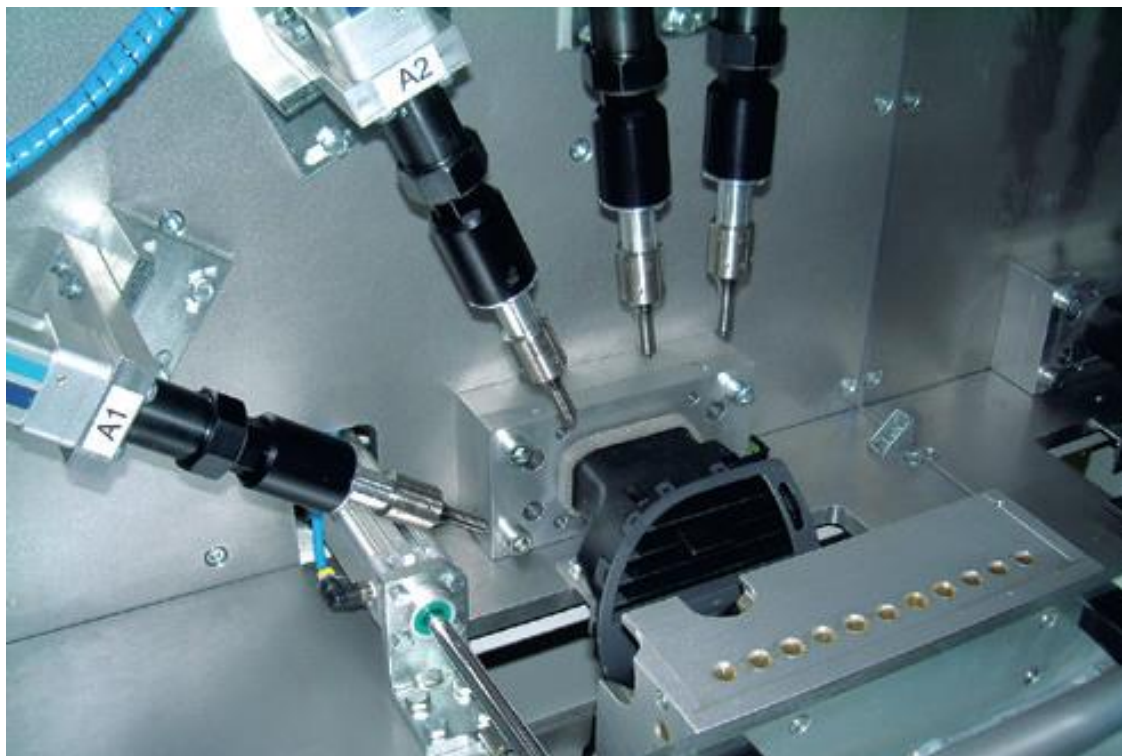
Многоточечная машина для ультразвуковой сварки компании «U-Sonic»
